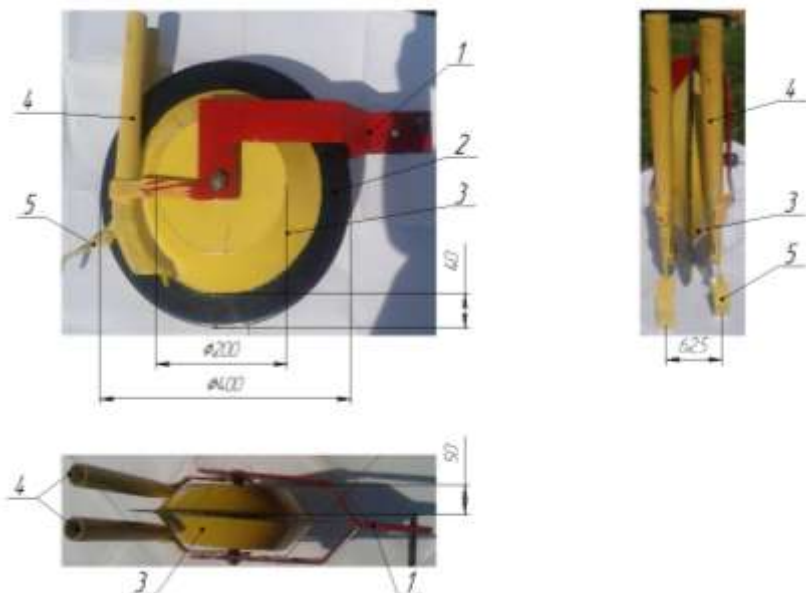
Новый макетный образец однодискового сошника с внешними симметричными ребрами-бороздкообразователями (вариант 2):
